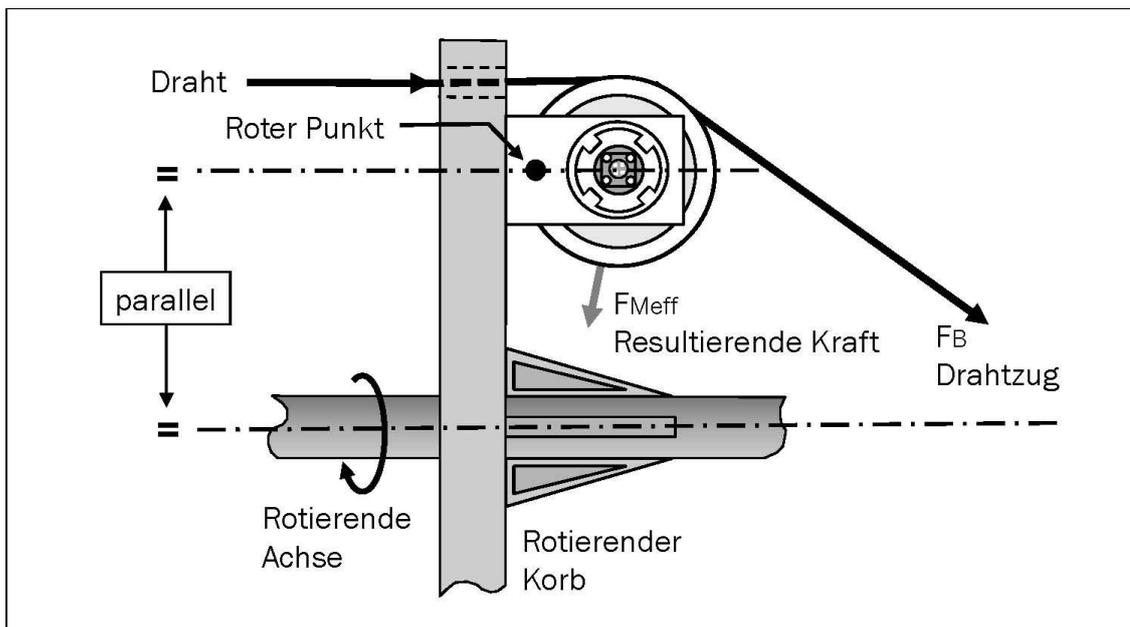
RMGZ Ausrichtung des roten Punktes in Verseilmaschinen R800004d
